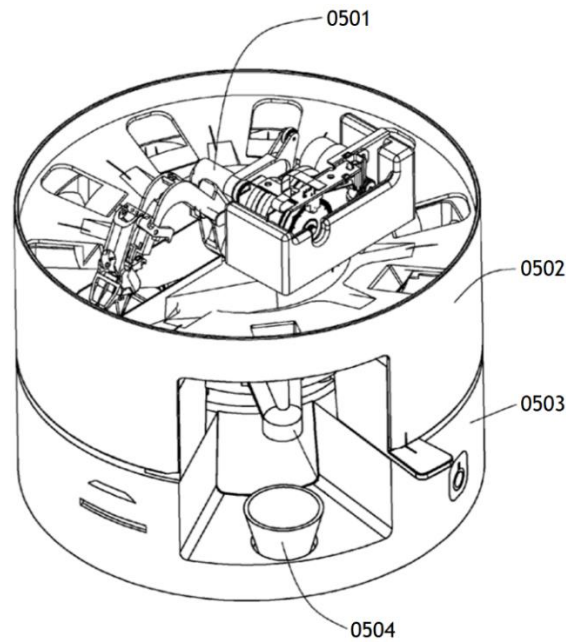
Desenho da patente US2014131378A1. Adaptado de [35]. 0501 - Conjunto de recolha de comprimidos; 0502 - Invólucro; 0503 - Chassis; 0504 - Caixa para dispensa de comprimidos.
